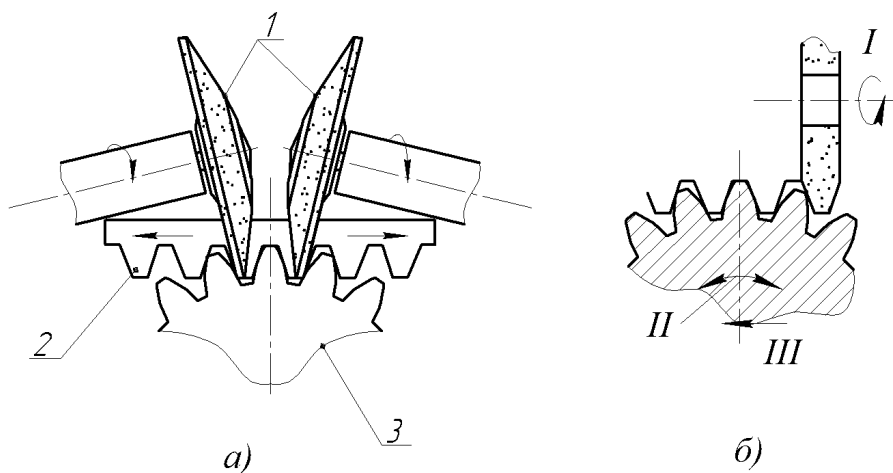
Схема шліфування зубів методом обкатки:
